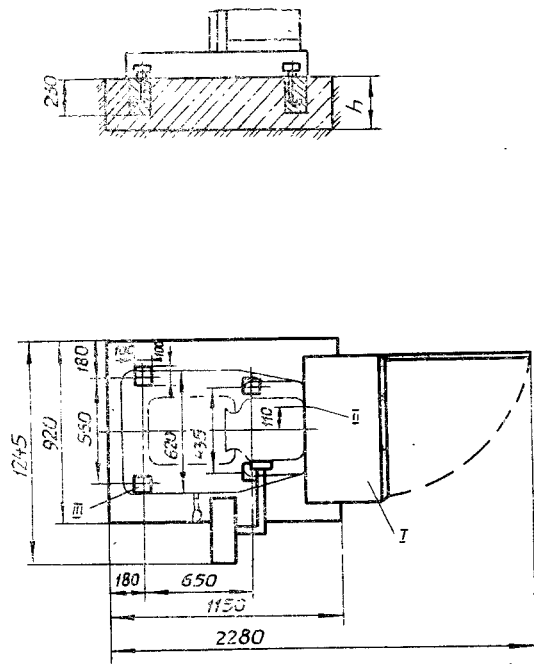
Габариты станка в плане и план фундамента станка 2С132ПФ2И.
